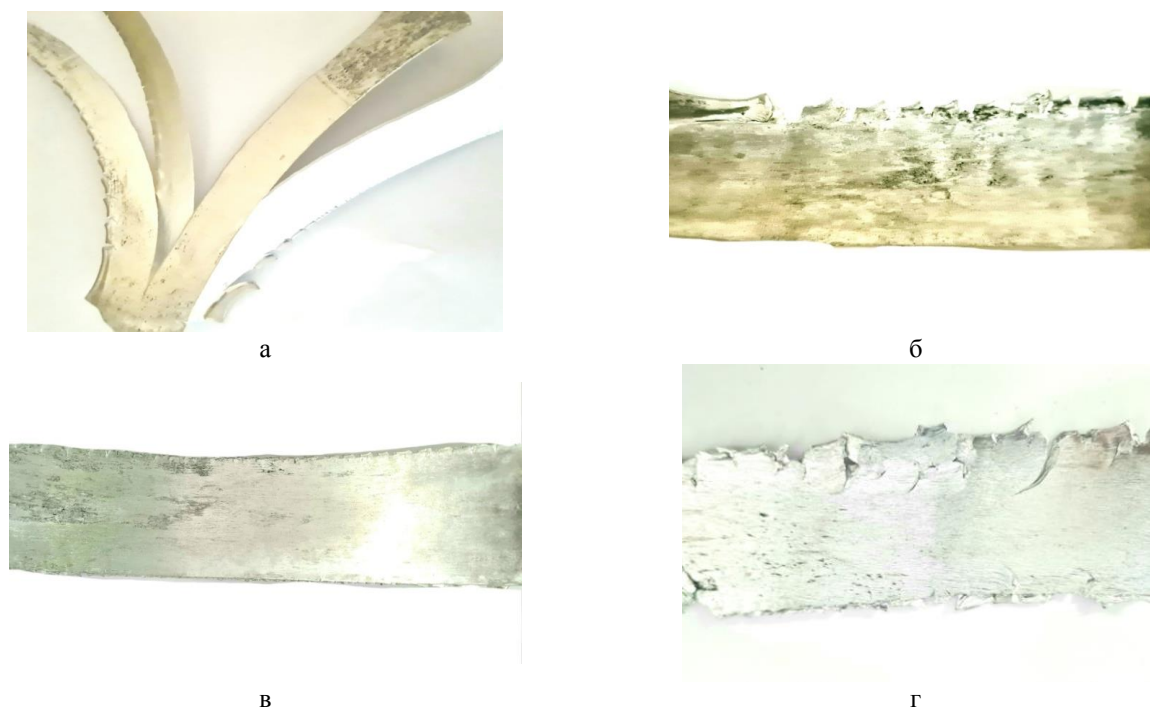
Образцы алюминиевых сплавов после симметричной и асимметричной деформации: а – образец 1; б – образец 2; в – образец 3; г – образец 6
